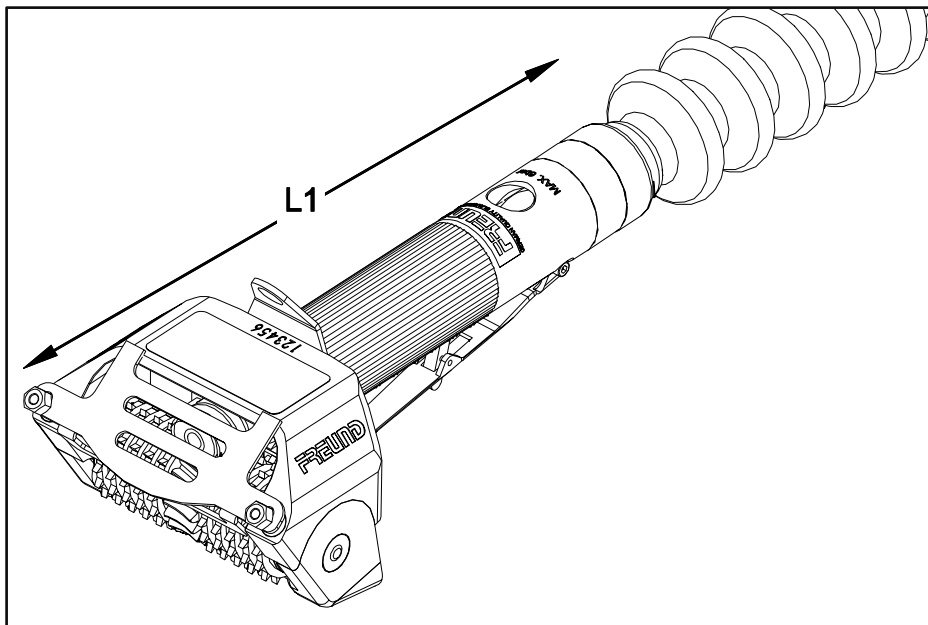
Hand-Skinner HSK8-P3 в сборе
